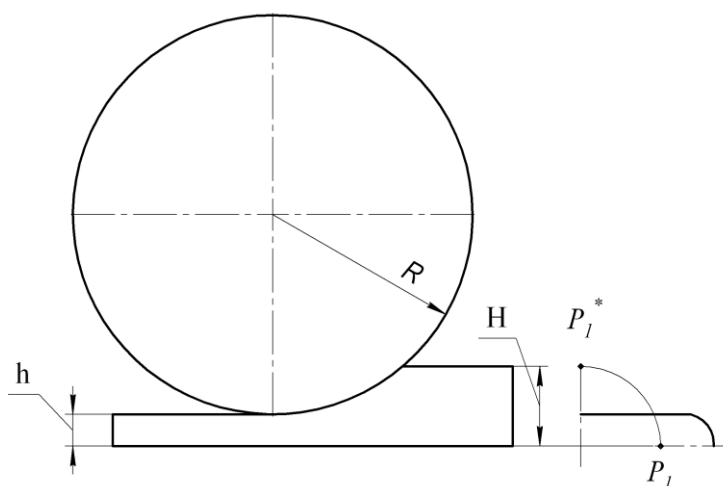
Схематичне представлення процесу вальцювання заготовок
